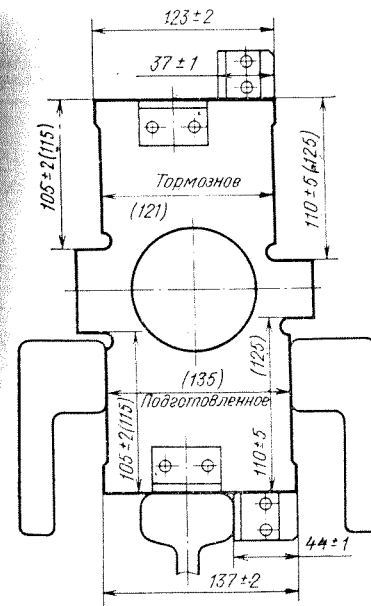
Шаблон для регулировки подготовленного и заторможенного положений замедлителя ВЗПГ
